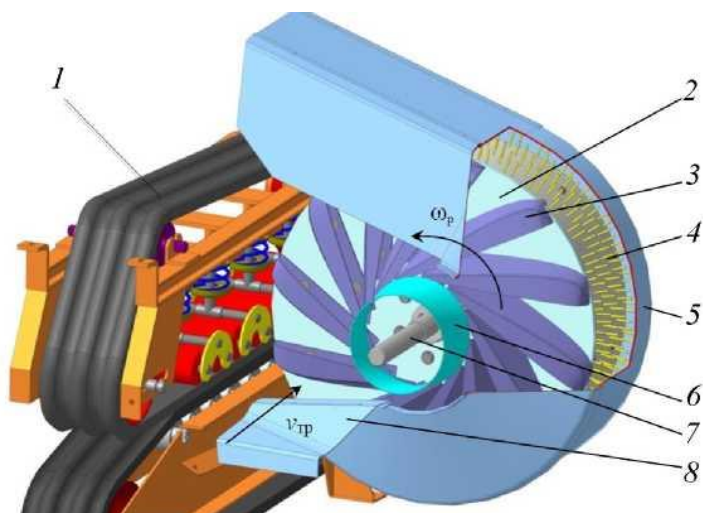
Конструкция роторно-бильного аппарата: 1 – зажимной транспортер; 2 – ротор; 3 – бичи; 4 – вычесывающе-транспортирующая щетка; 5 – кожух; 6 – кольцо; 7 – вал ротора; 8 – стол
